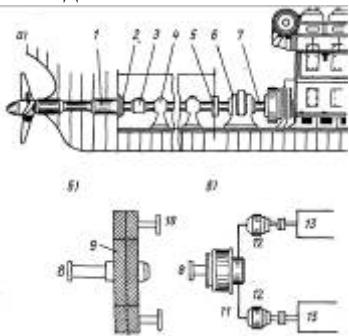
Различные варианты передачи энергии к гребному винту: а — прямая; б — редукторная; в — электрическая. 1 — гребной вал; 2 — сальник; 3 — полумуфта; 4 — опорный подшипник; 5 — переборочный сальник; 6 — упорный подшипник; 7 — упорный вал; 8 — к фланцу гребного вала; 9 — редуктор; 10 — к фланцу двигателя; 11 — гребной электродвигатель; 12 — генератор; 13 — двигатель
